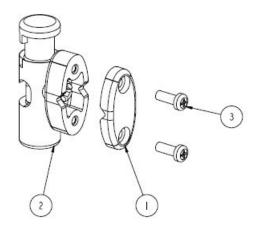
Remplacement des pièces du clip du cordon pour serre-tête
